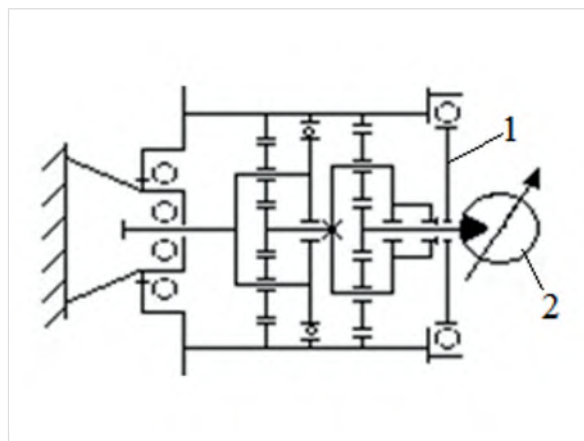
Схема привода лебедки грузоподъемного механизма крана: 1 — барабан лебедки с встроенным планетарным редуктором; 2 — гидродвигатель
